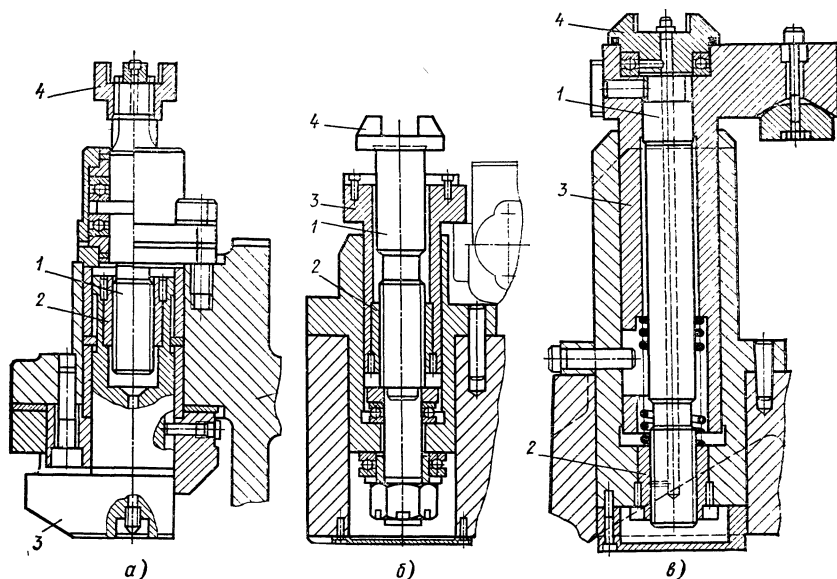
Конструкции прихватов на приспособлениях-спутниках:
